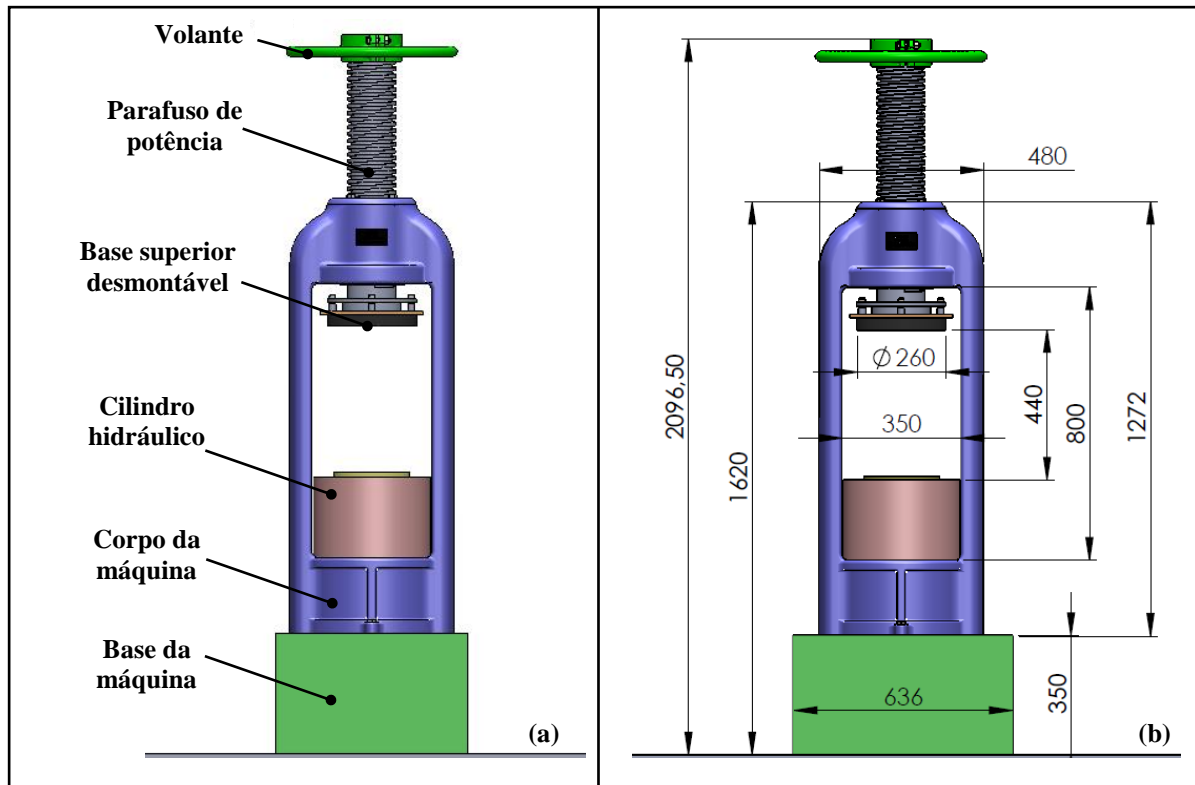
Principais componentes da máquina de compressão (a); principais dimensões em milímetros da máquina compressão (b).
